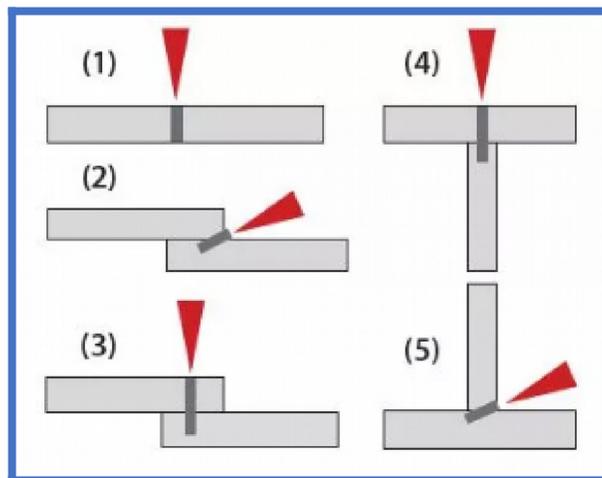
La soldadura láser ofrece diversas configuraciones de juntas: a tope (1); a solape, ya sea a lo largo de la costura (2) o a través de la chapa superior (3); y en T, a través de la chapa superior (4) o desde un solo lado (5). Fuente.
